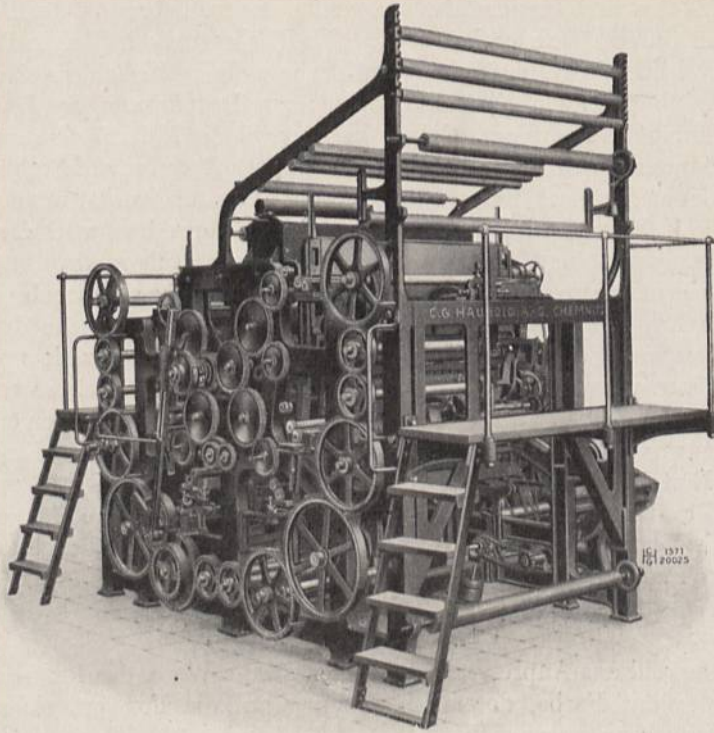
2×3-Farbendruckdruckperrotine. (Haubold.)
